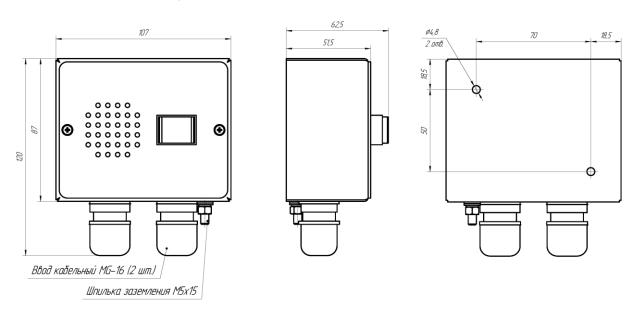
Габаритные и установочные размеры БС-106
